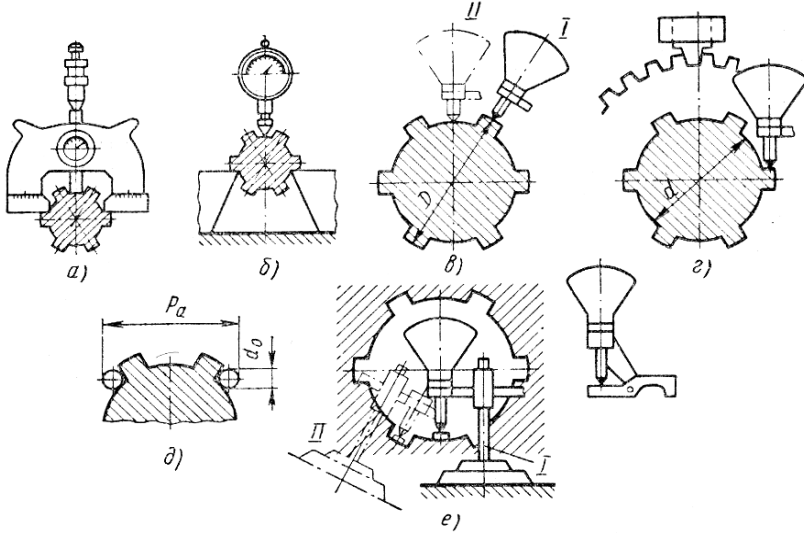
Контроль елементів шліцьового з'єднання.
